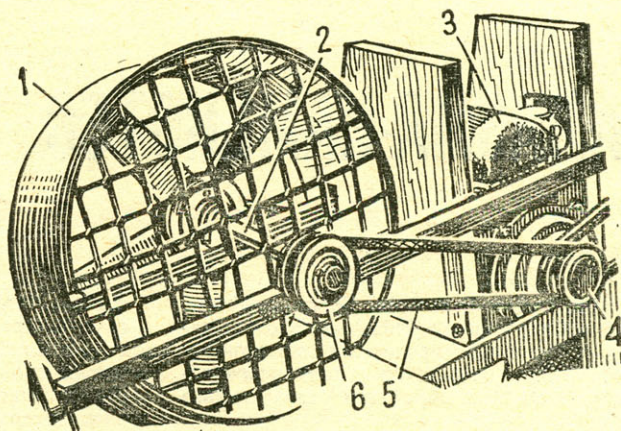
Винтомоторная установка (вид спереди): 1 — аэродинамическое кольцо, 2 — вал вентилятора, 3 — двигатель «Ллойд», 4 — двойной шкив на валу двигателя, 5 — текстурный приводной ремень, 6 — шкив на валу вентилятора.
